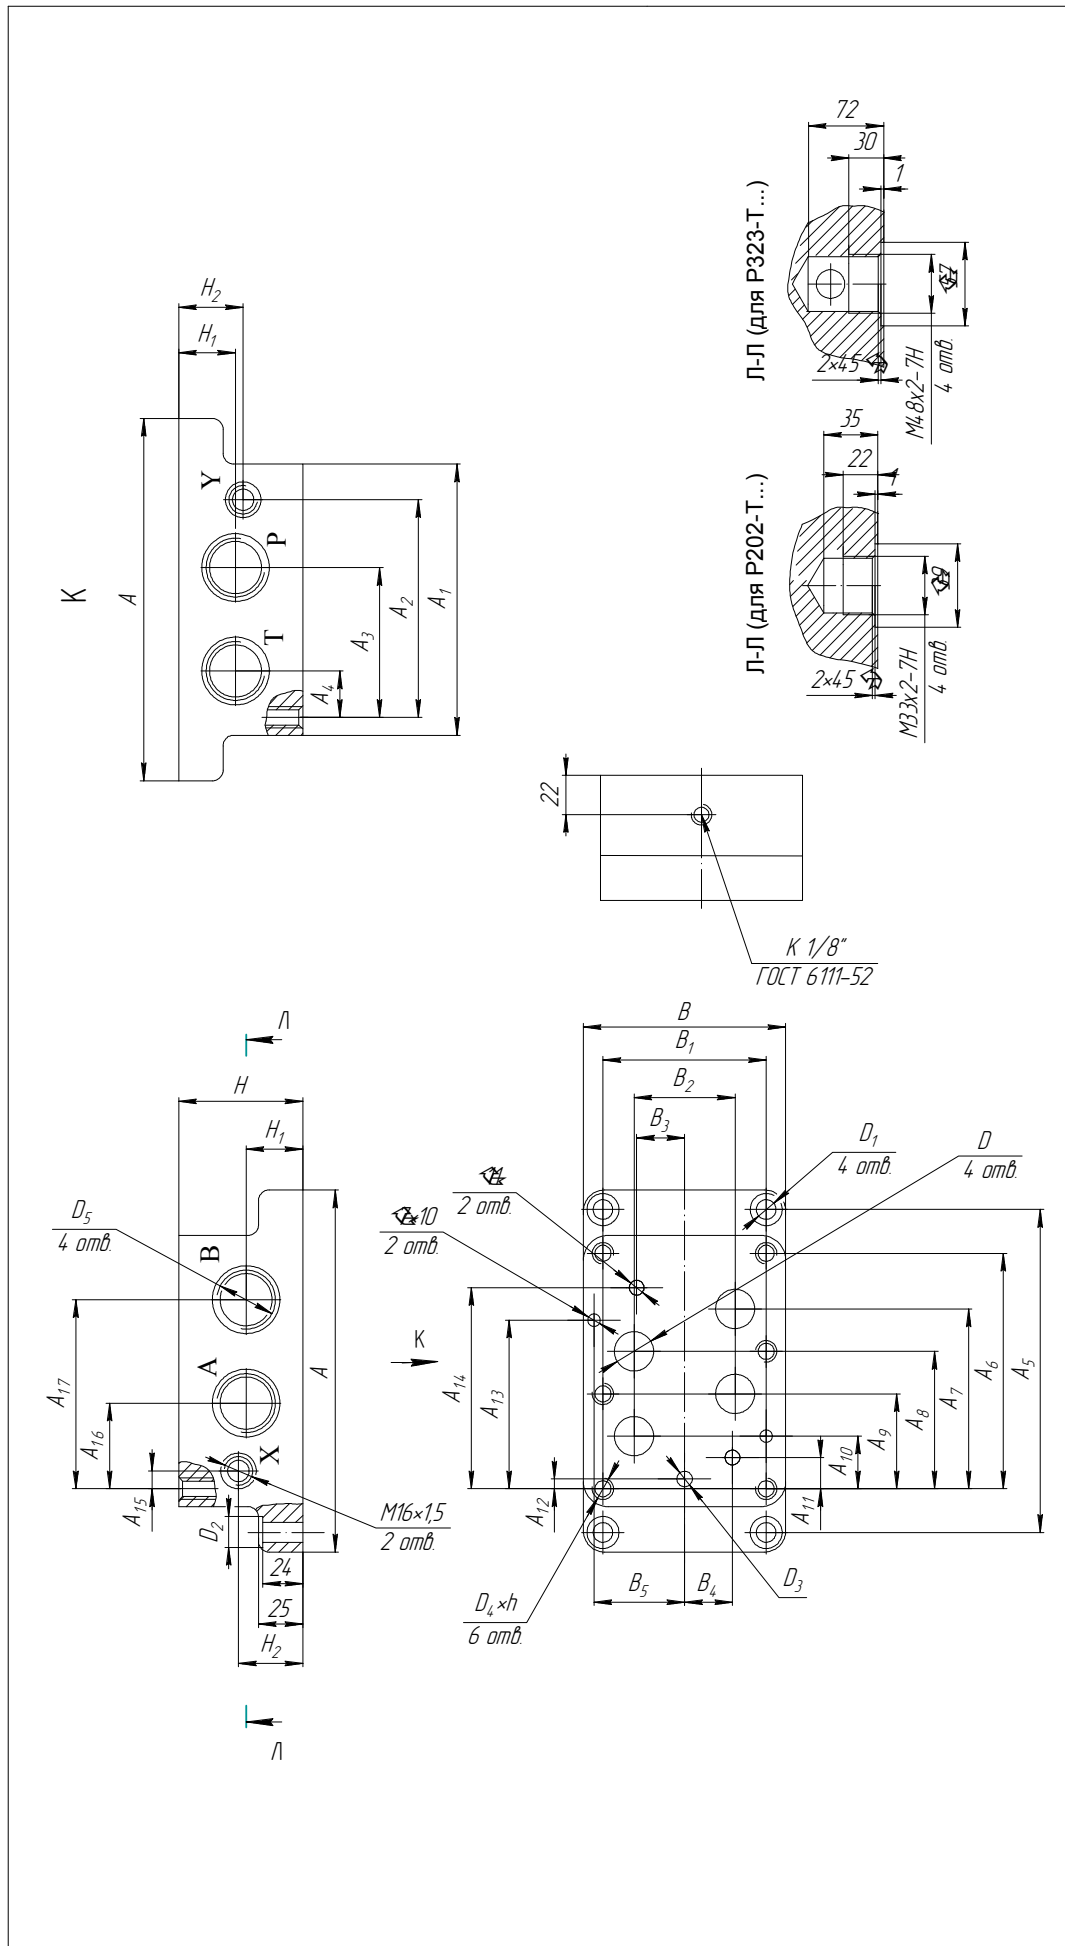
Габаритные и присоединительные размеры присоединительных плит.
